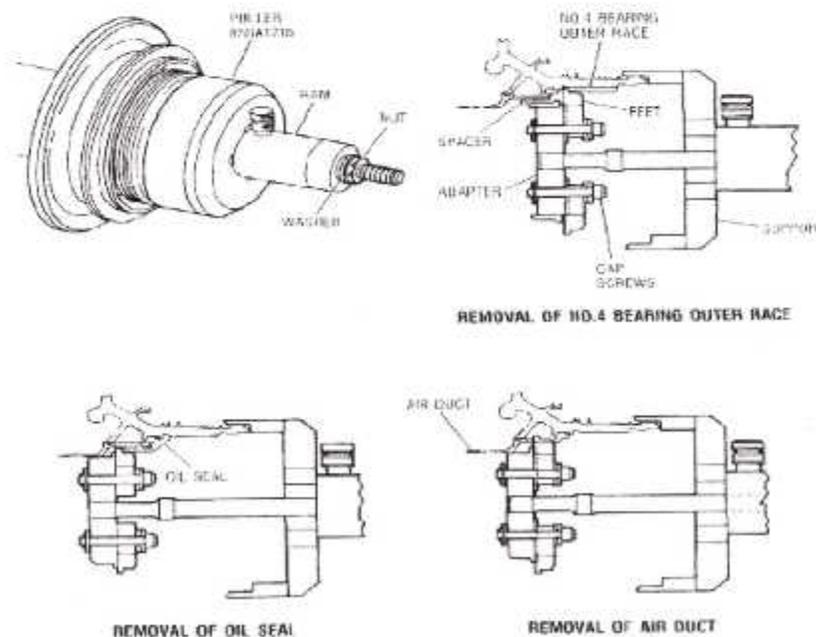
Dépose de la Cage Extérieure du Roulement.04, Joint de Retenue d'Huile et la tuyère d'Air.
